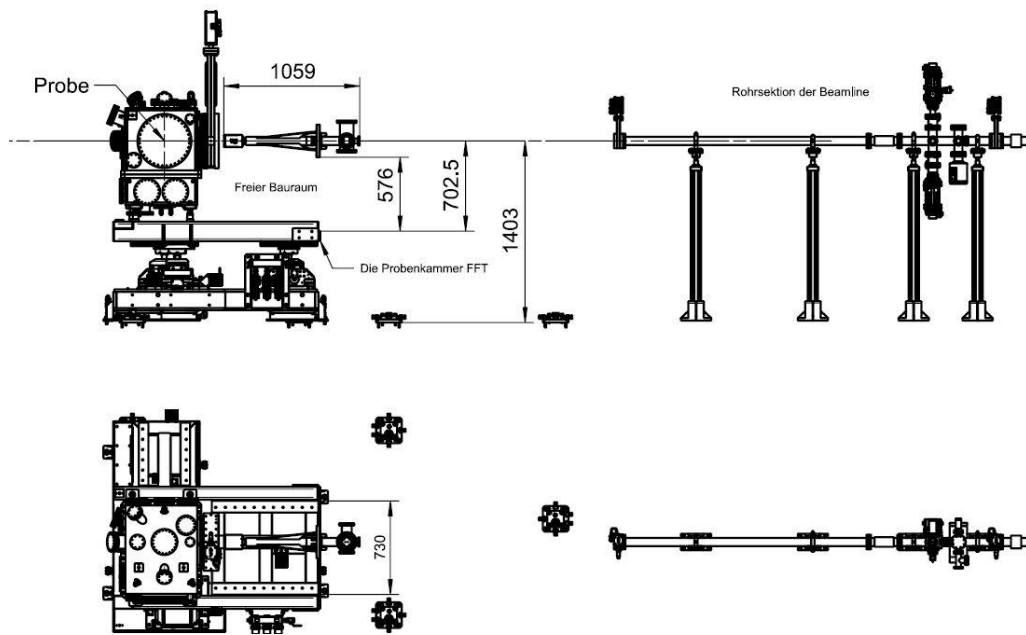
Bauraum für die Integration der FastCCD in der SCS-Beamline (Drauf- und Seitenansicht)
